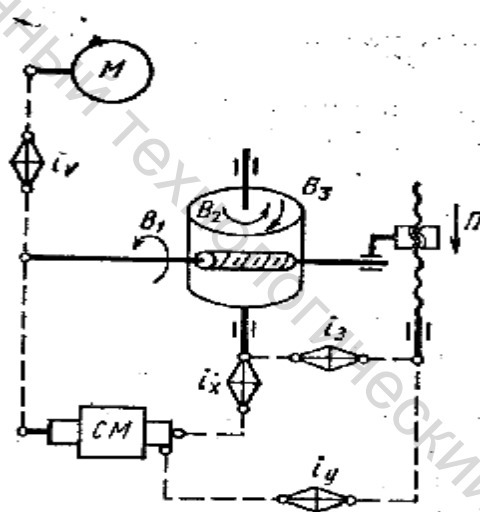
Формаобразующие движения в зубофрезерном станке.
